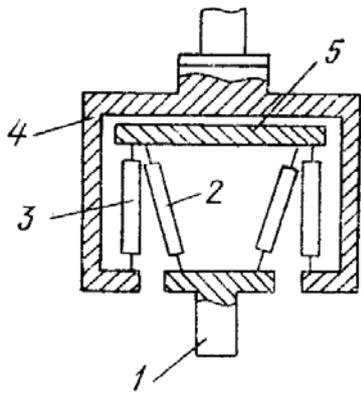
Пассивное адаптивное устройство для установки деталей
